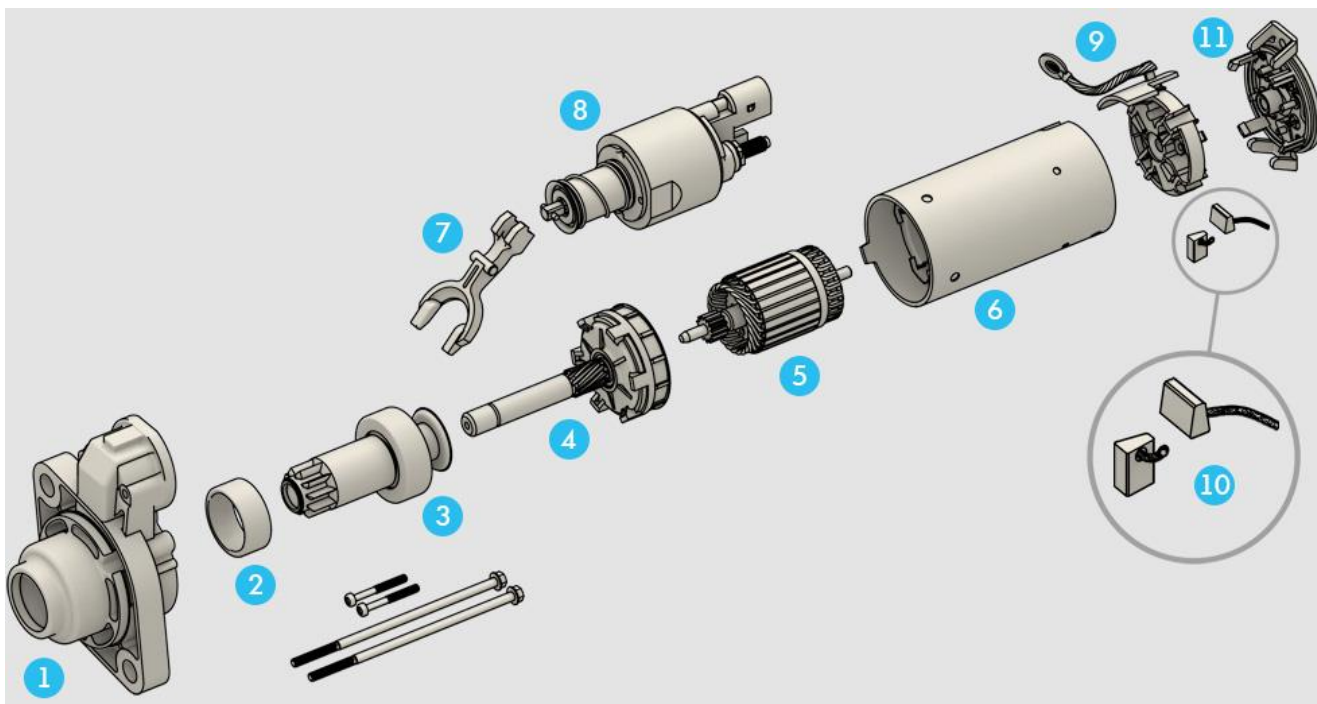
будова стартера автомобіля: 1 – кришка передня (маска); 2 – втулка стартера; 3 – бендикс; 4 – редуктор; 5 – якір; 6 – корпус; 7 – вилка; 8 – втягуюче реле; 9 – щітковий вузол; 10 – щітки; 11 – задня кришка.
